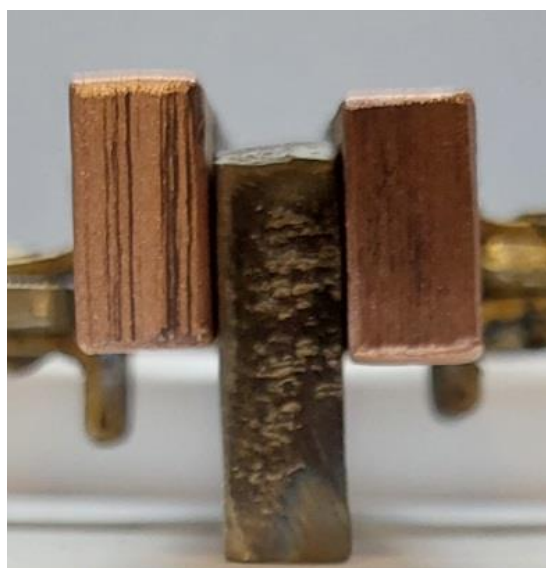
Схема сборки под наплавку торцевых поверхностей с применением медных формирующих пластин
